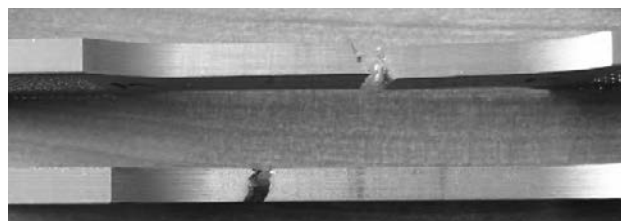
Геометрия разрыва сварного шва образцов 1* и 2
